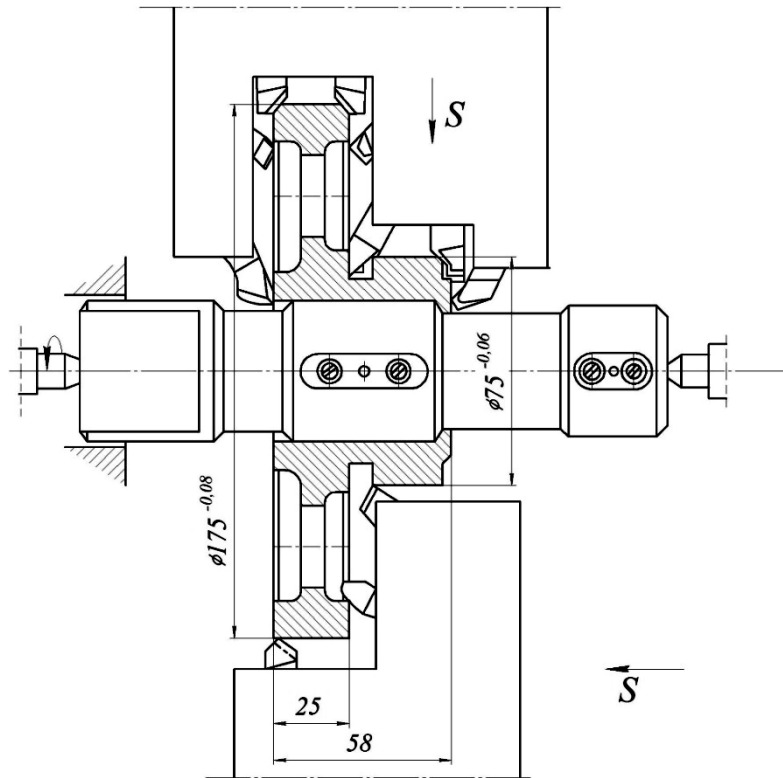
Схема налагодження для оброблення блоку зубчастих коліс на одношпindelному багато різцевому токарному напівавтоматі
